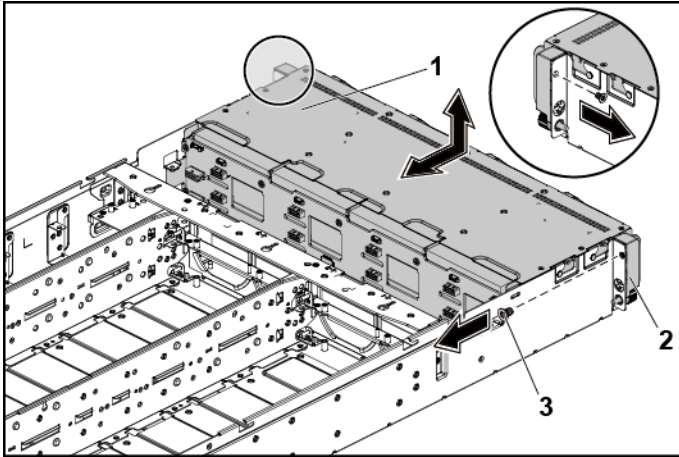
Extracción e instalación del plano posterior directo
